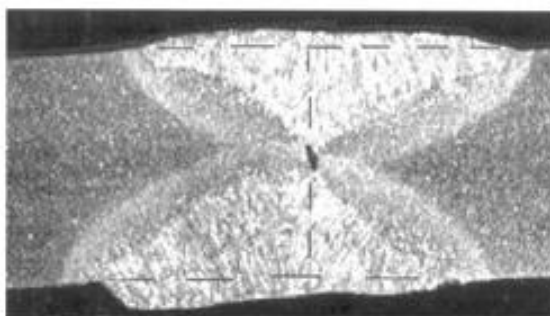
Macrografia de uma junta soldada por fusão.
